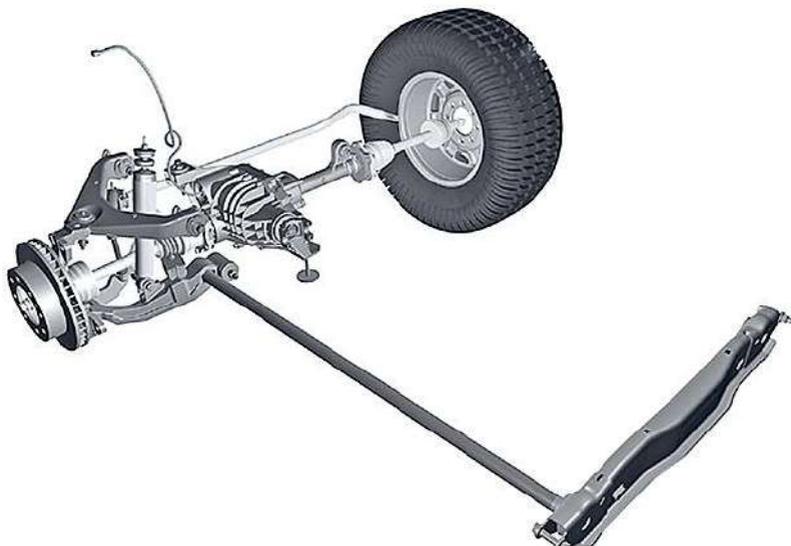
Підвіска з поздовжньо розташованим торсіоном (довгим стрижнем, закріпленим спереду на важелі, ззаду – на поперечині кузова)
